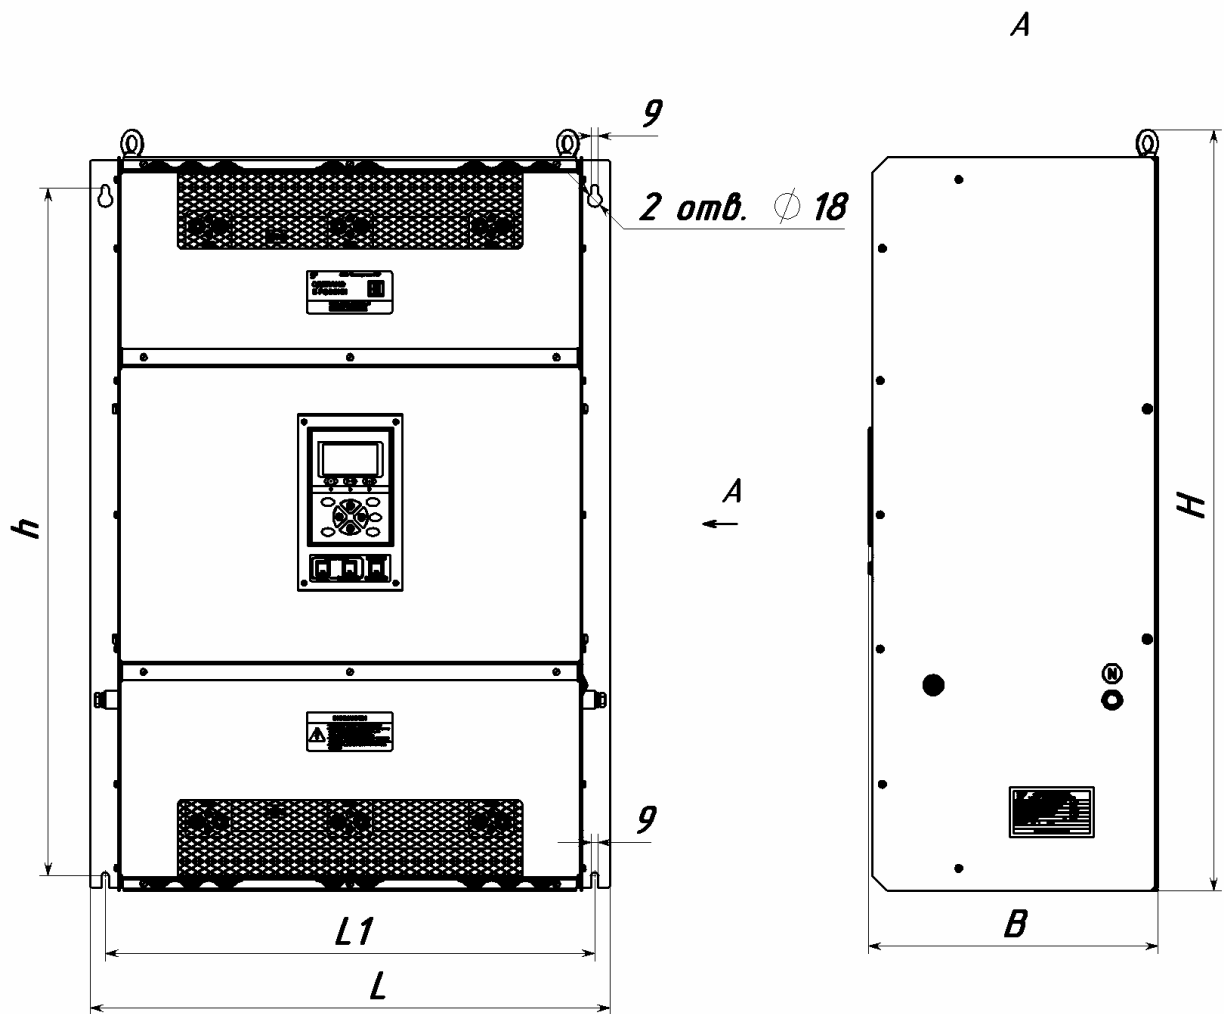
д – Габаритные и установочные размеры УПП 315-400 кВт
